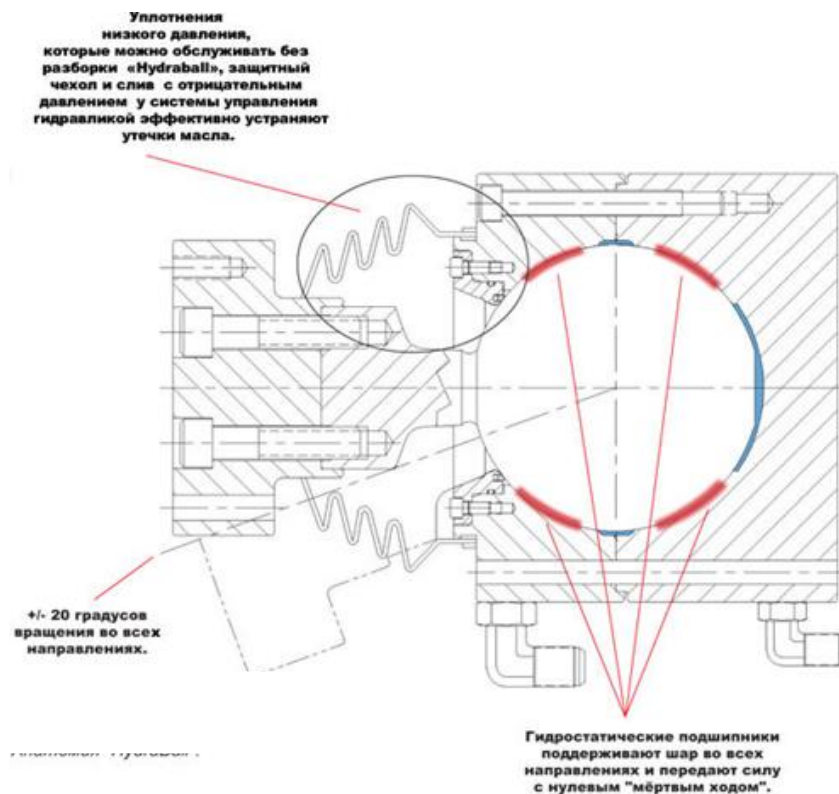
Шаровой шарнир с гидростатическими подшипниками [25]
